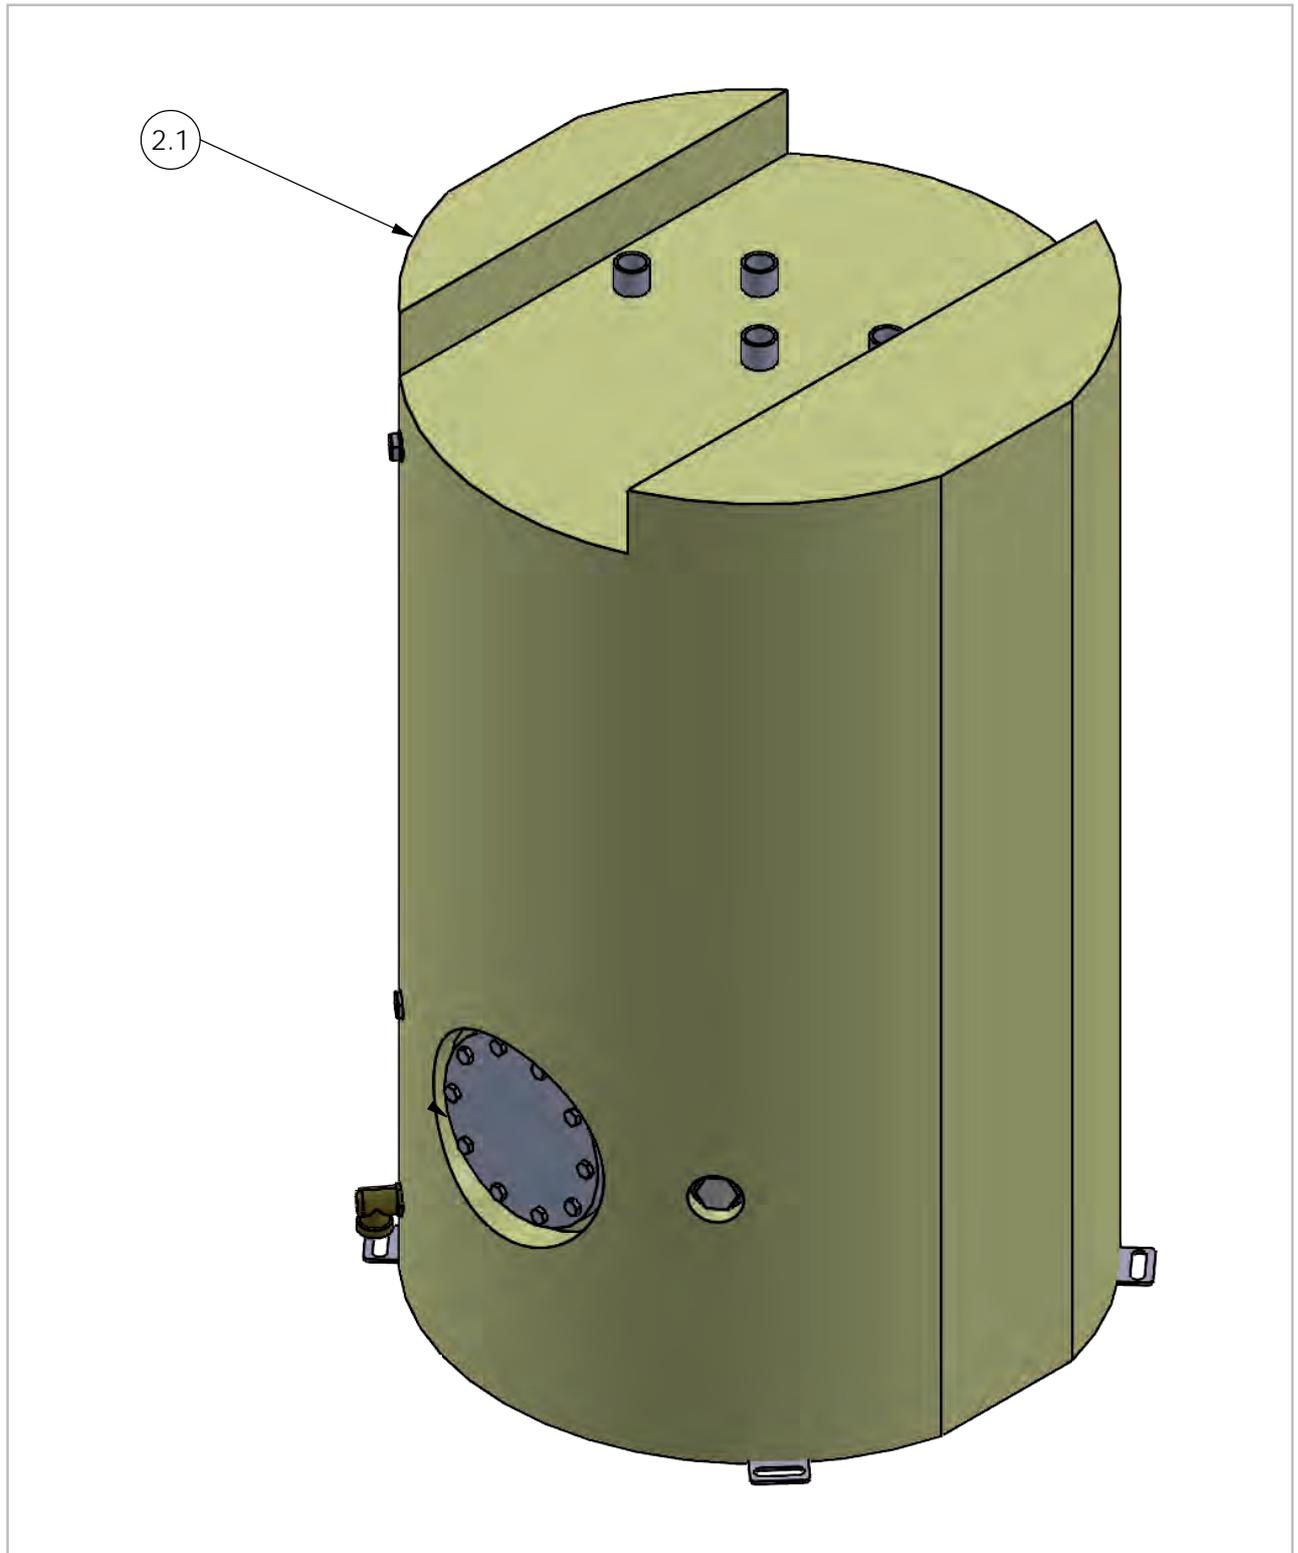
Explosionszeichnung Speichermodul MTS 150
